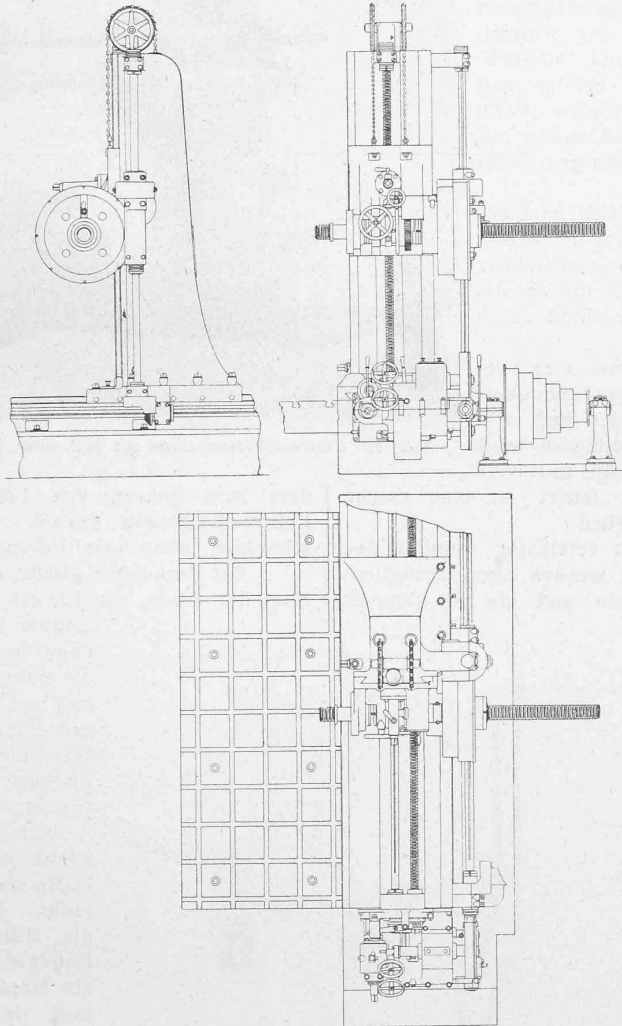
Horizontale Bohr- und Fräsmaschine.
